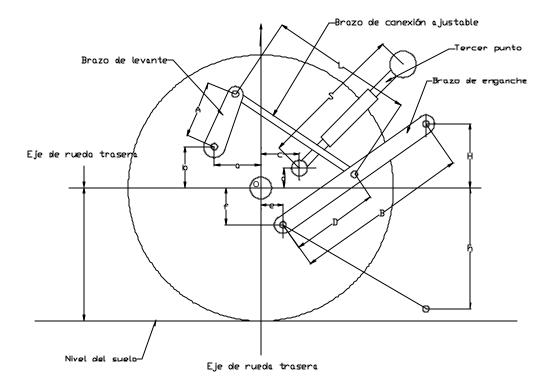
Prueba de levante – Geometría del enganche de tres puntos
